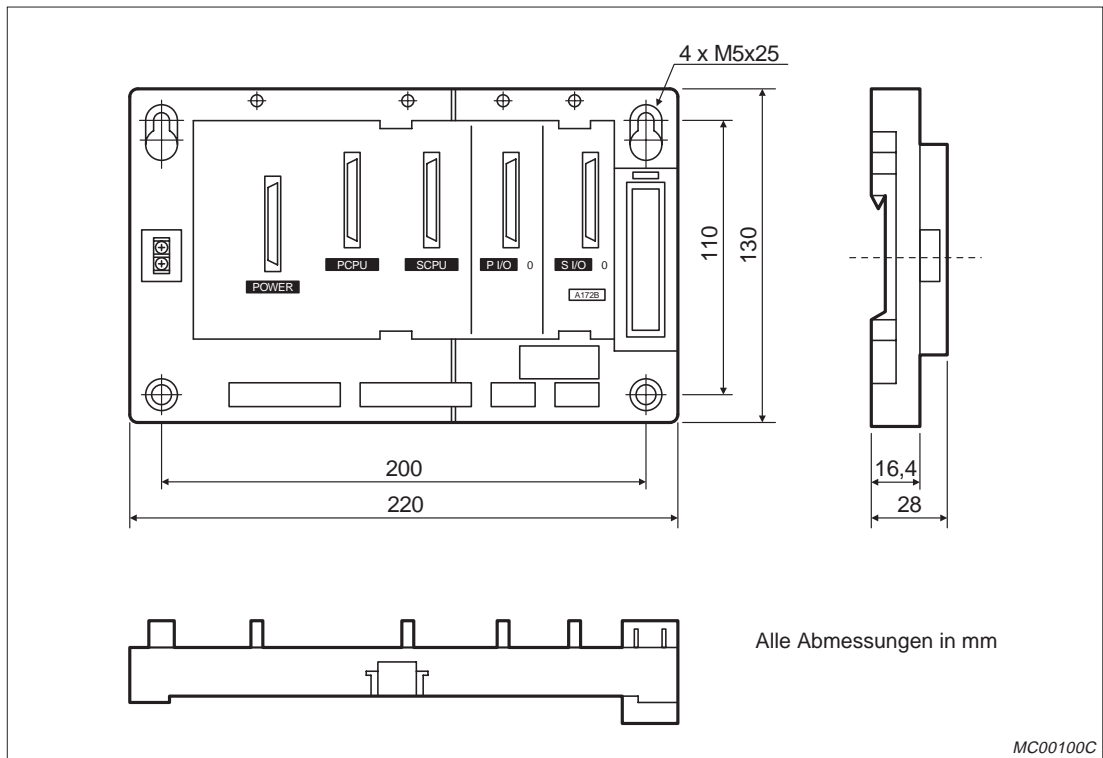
Abmessungen des Hauptbaugruppenträgers A172B
